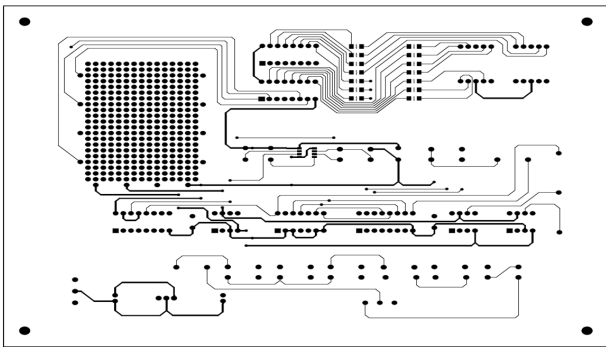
개별 실습자를 위한 회로 설계 PCB
